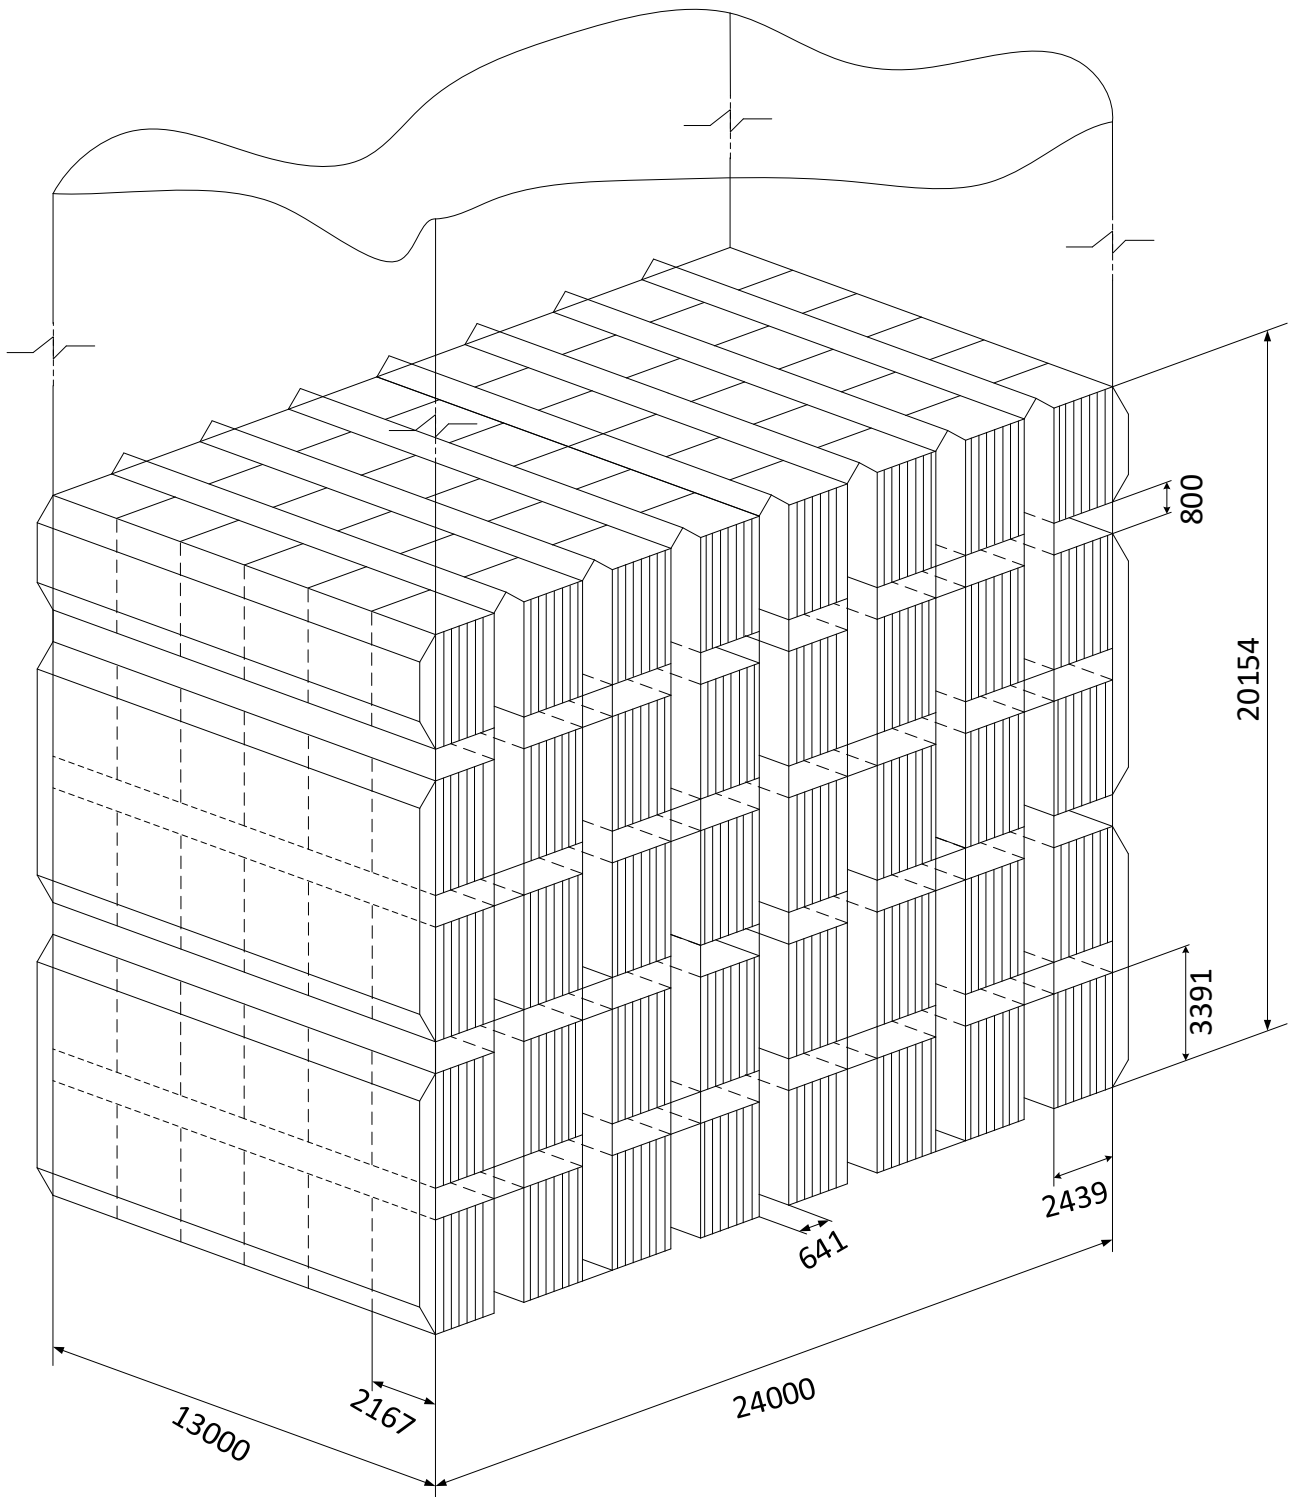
Конструктивный эскиз трубчатого воздухоподогревателя
